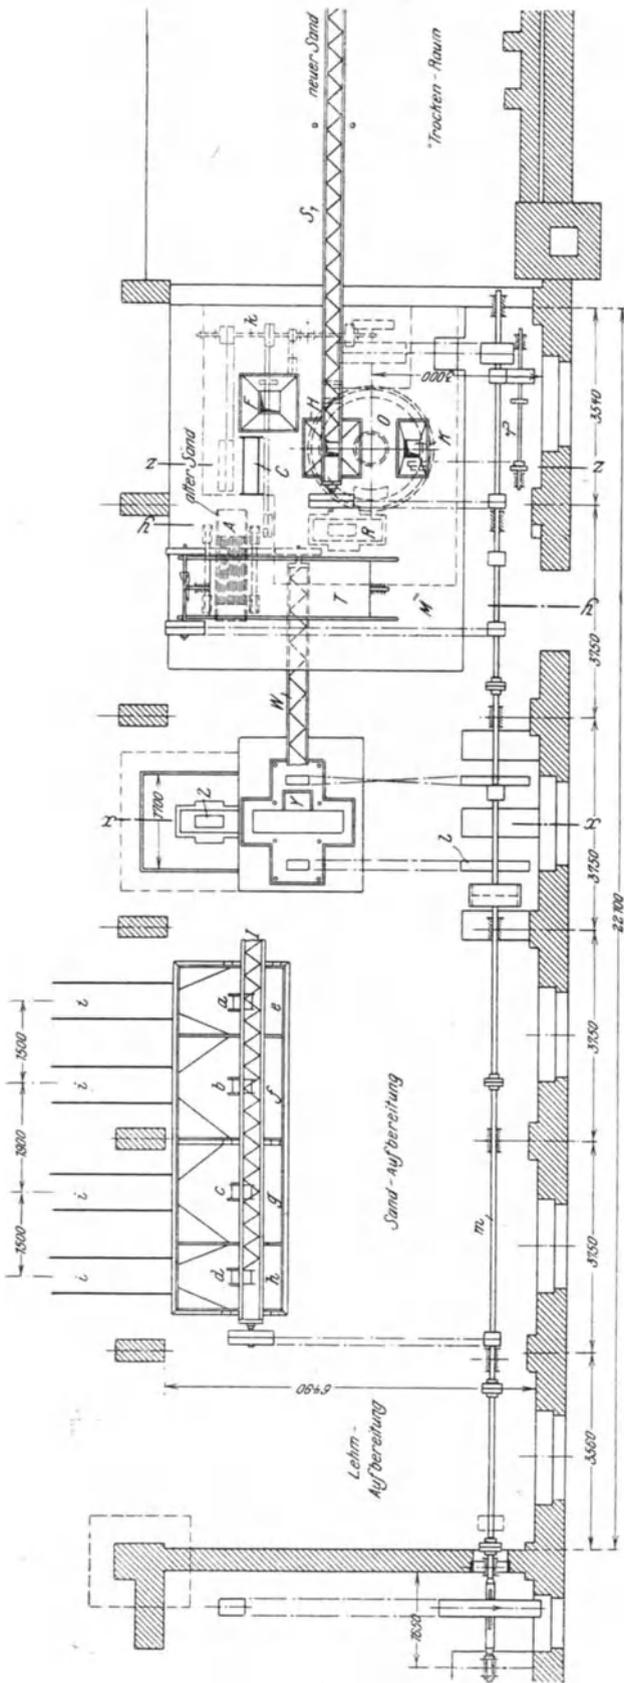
Grundriß einer selbsttätigen Sandaufbereitung, Bauart Brinck & Hübner.
